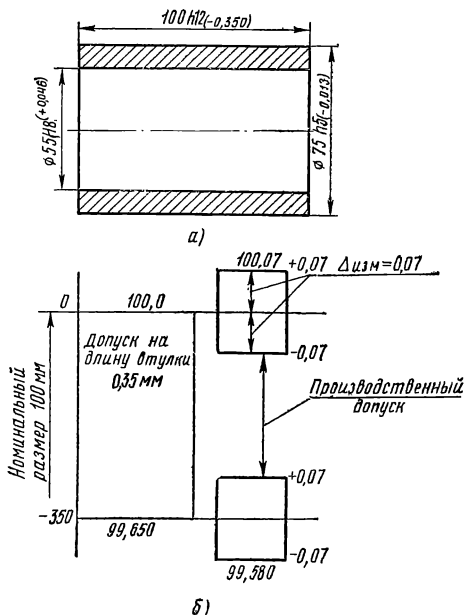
Эскиз втулки (а), схема расположения поля допуска детали и погрешности измерения (б)
